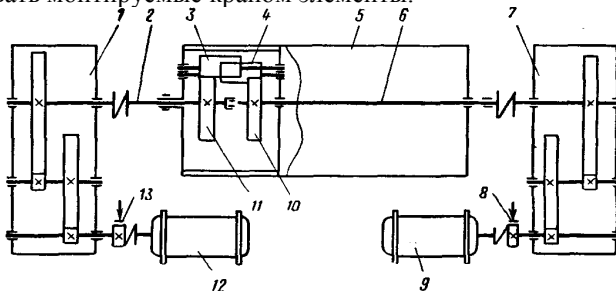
Схема многоскоростного механизма подъема башенного крана: 1 – редуктор; 2 – вал; 3,4,10,11 – шестерни планетарного редуктора; 5 – барабан; 6 – вал; 7 – тормоз; 9, 12 – электродвигатели; 13 – тормоз
